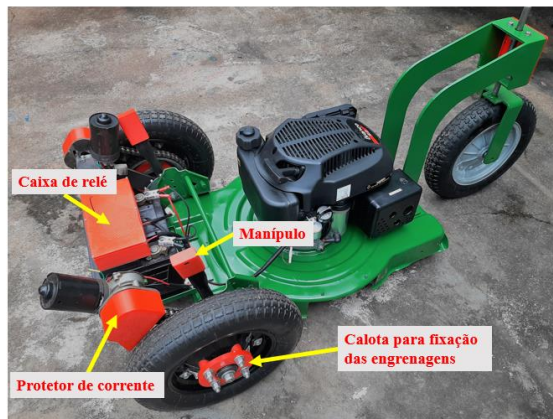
Componentes fabricados em impressora 3D e a montagem completa.
